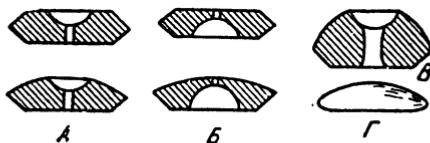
Разновидности часовых камней: А—сквозные; Б—сквозные балансовые; В—сквозной для оси центрального колеса; Г—накладной
